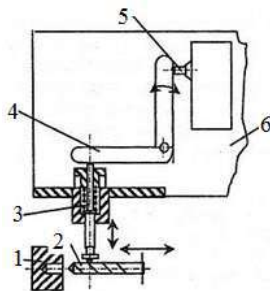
Схема контроля режущего инструмента на многоцелевом станке: 1 - заготовка; 2 - инструмент; 3 - контактный щуп; 4 - рычаг; 5 - электроконтактный датчик; 6 - многоцелевой станок
